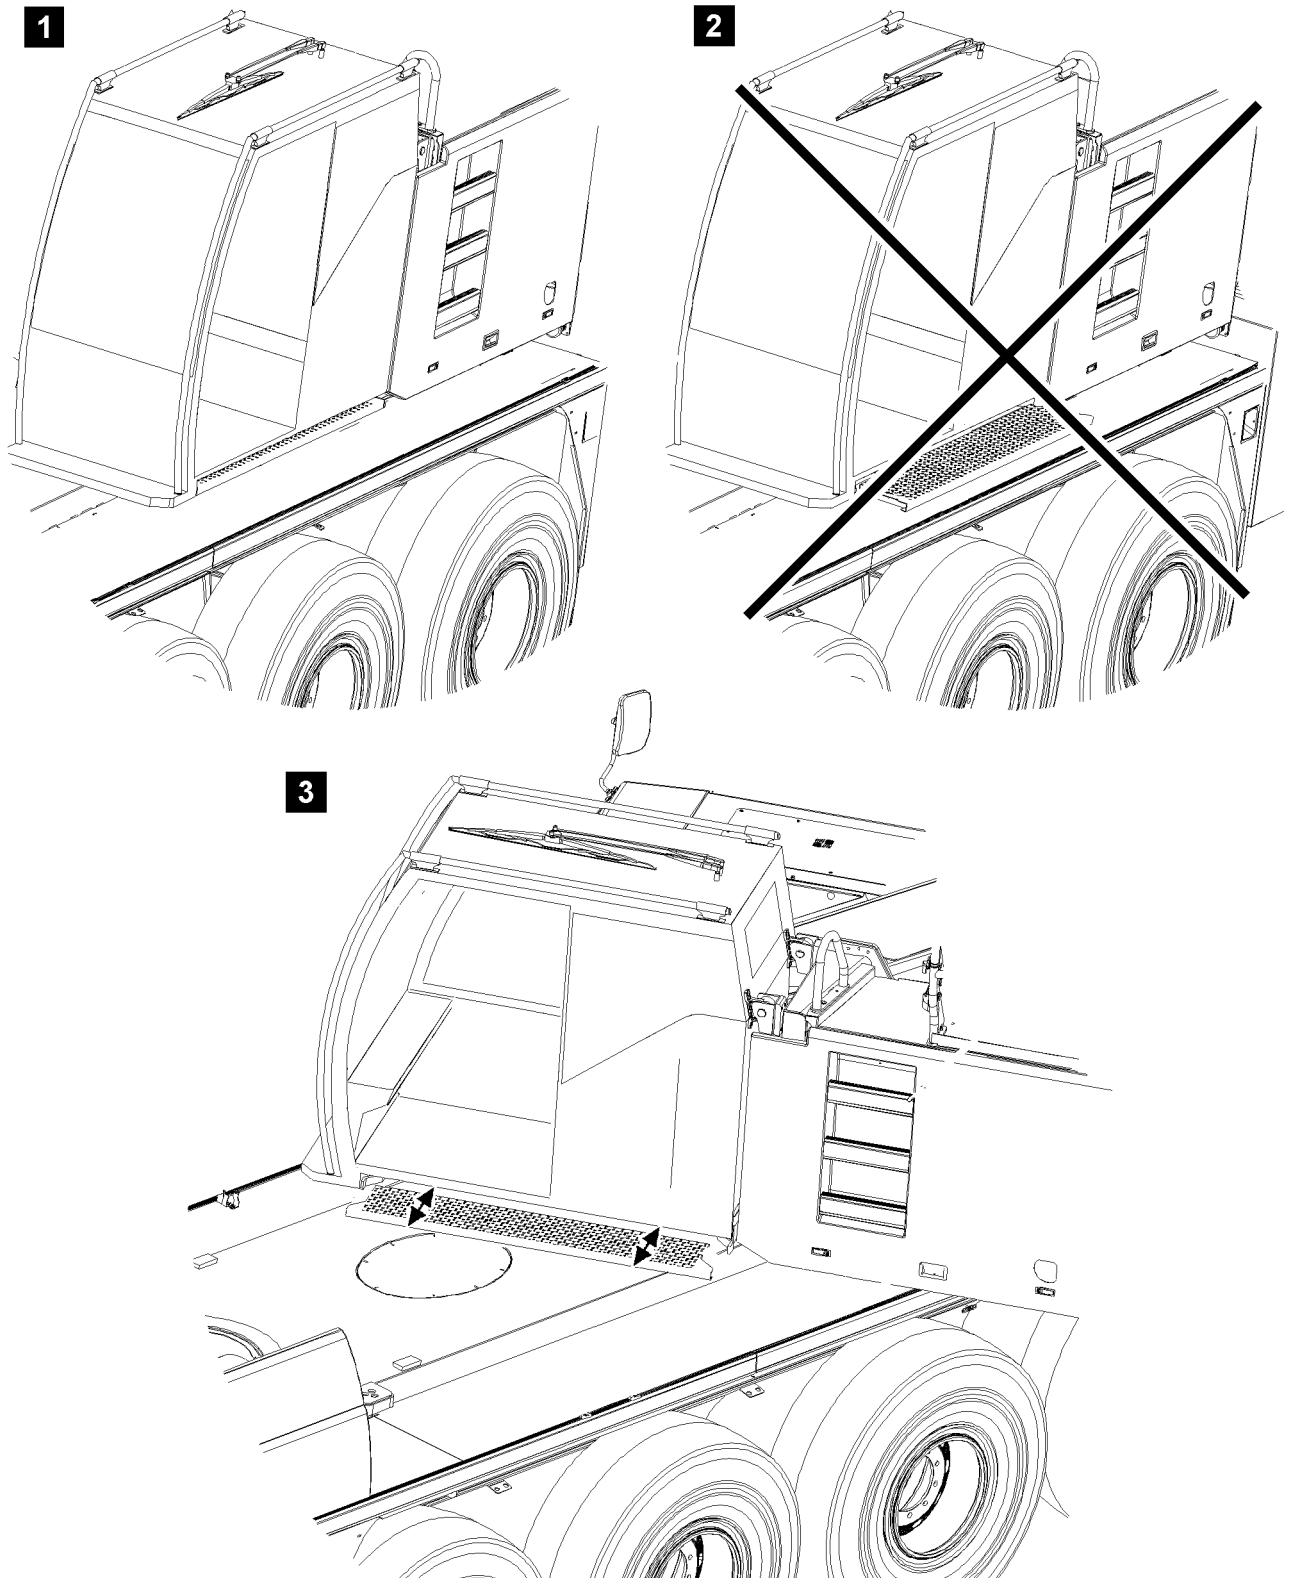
Exemplo de cabine de guindaste com estribo rebatível para dentro/fora
